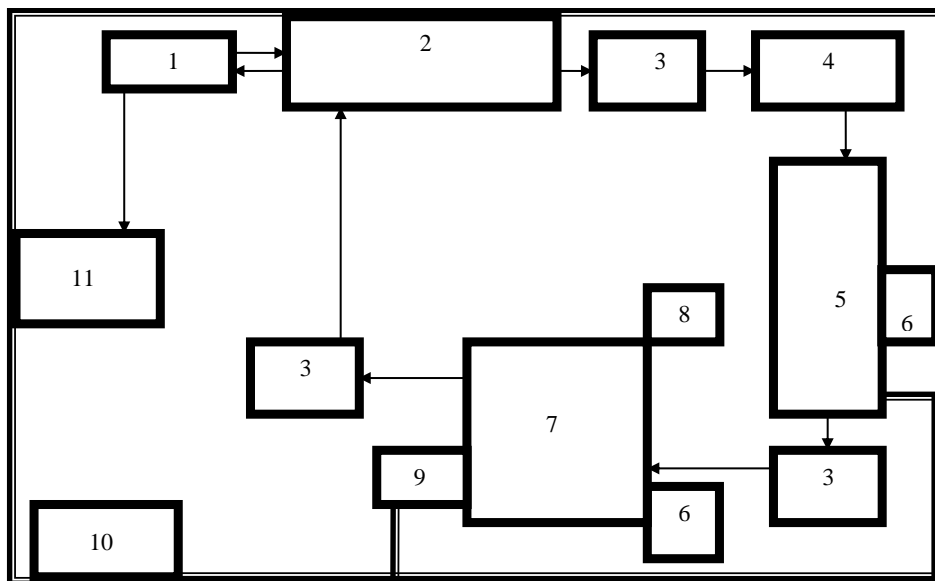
Компоновка обладнання дільниці відновлення колінчастих валів: 1 - стіл для дефектування деталей, 2 - спеціалізований верстат для перешліфовки колінчастих валів, 3 - верстат слюсарний; 4 - камера для очищення і знежирення деталей, 5 - камера абразивно-струменевої обробки, 6 - система очищення відпрацьованого газу, 7 - камера ЕДН, 8 - джерело струму, 9 - система очищення і відділення вологи з транспортуючого газу, 10 - компресор та система стисненого повітря тиском 0,6 МПа., 11 - ванна насичення.
